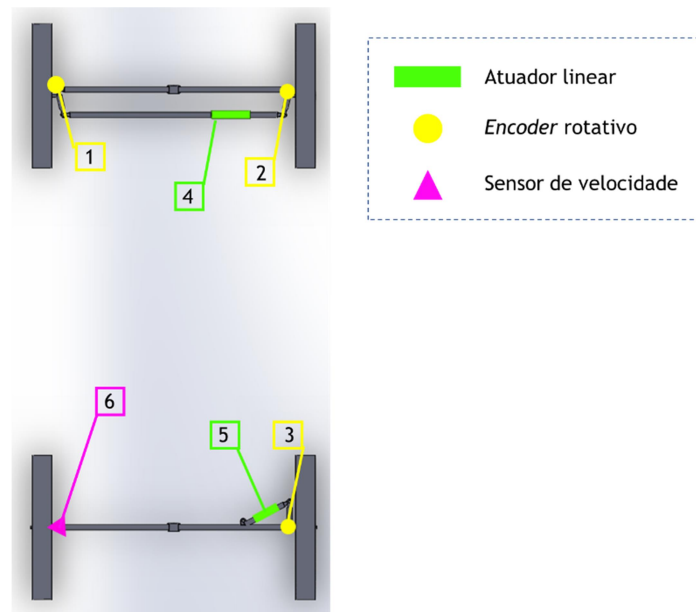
Posição dos componentes a instalar conforme a proposta de correção.
